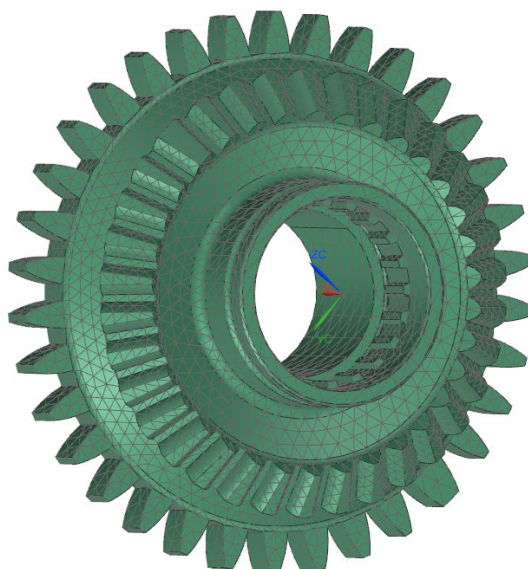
Розбивка на сітку кінцевих елементів деталі шестерня конічна
